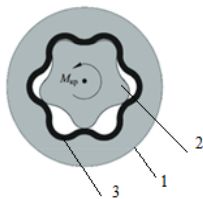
Конструкция винтового забойного двигателя: 1 – статор, 2 – ротор, 3 – эластомерная обкладка
